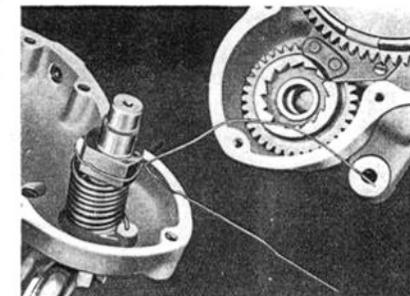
Mit einem Stück Bindendraht wird die Sperrklinke in der Anwerfvorrichtung zurückgehalten, um den mühe-losen Einbau in das Anwerfzahnrad zu ermöglichen.
